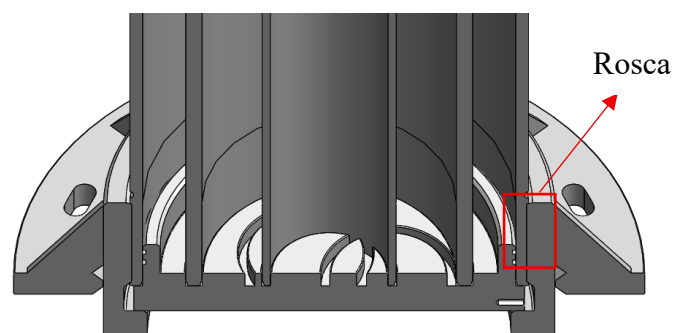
Montagem do cap inferior - Plug Inferior - Conjunto de tubos.
